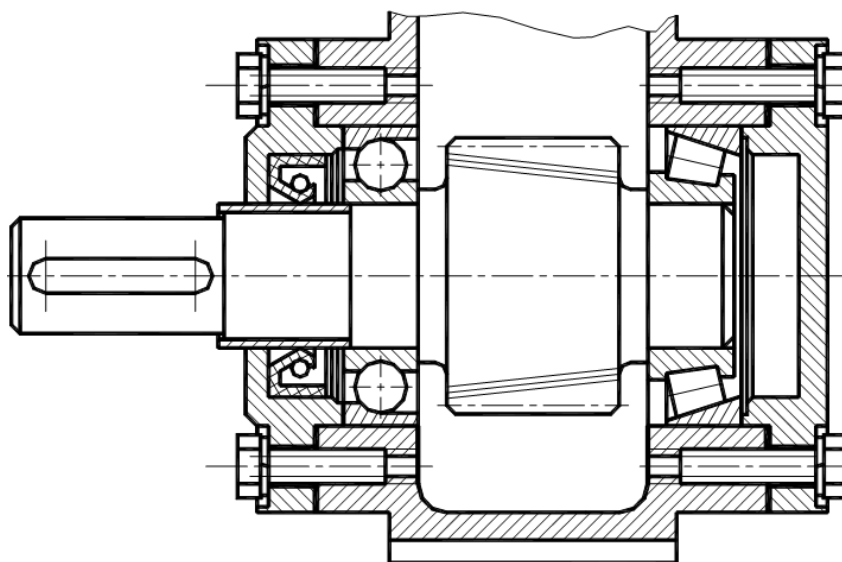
Установка вала на радиально-упорных подшипниках "враспор"
